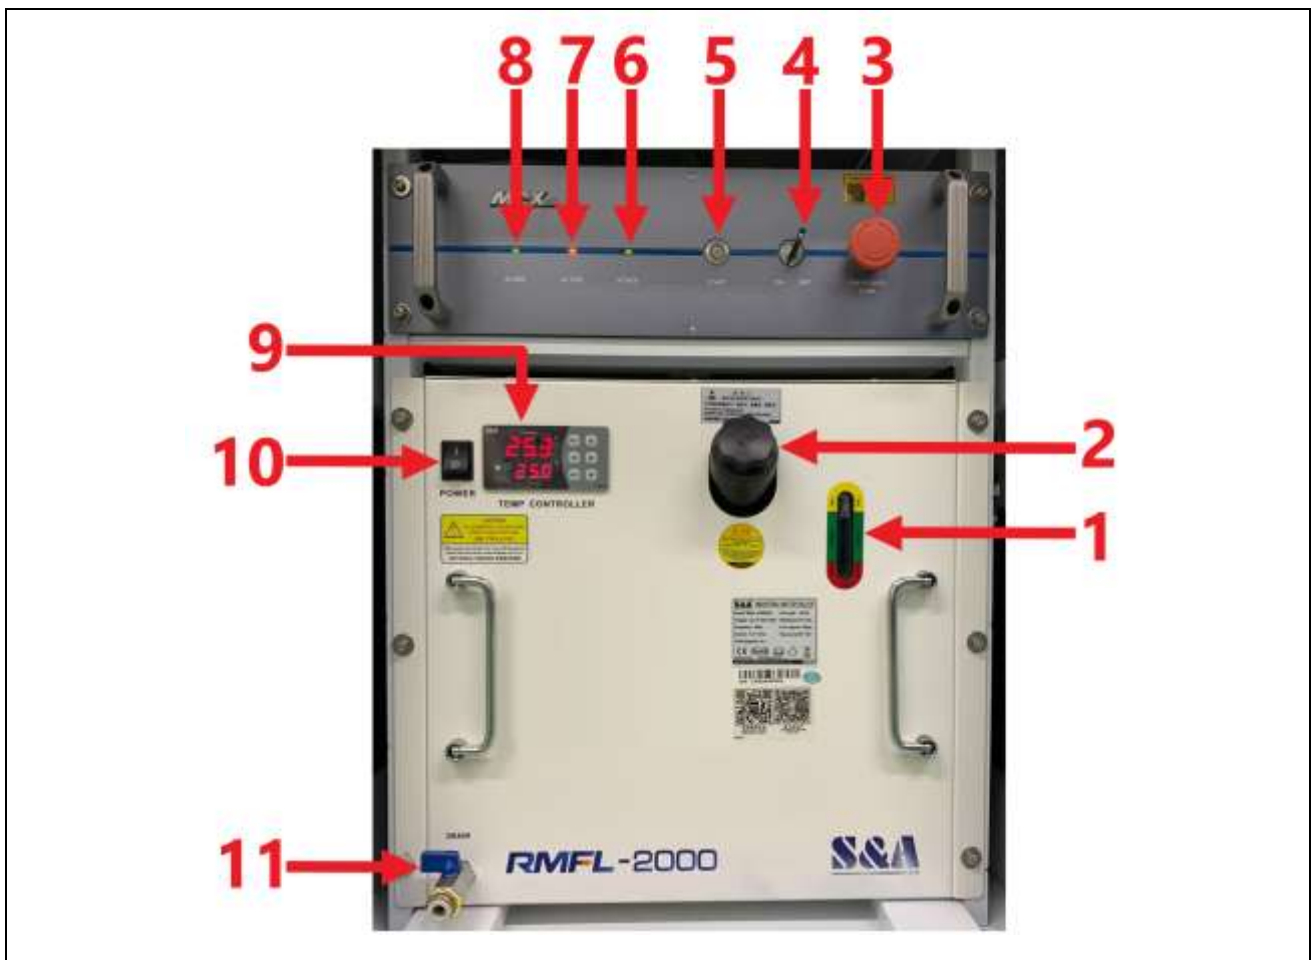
Vista frontal interna Vulcano Laser 2000.
